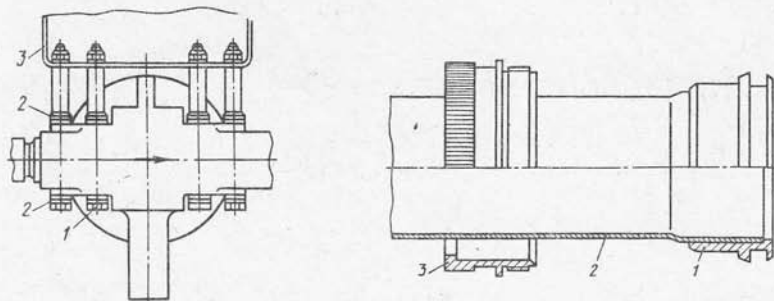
11. Установка агрегата на кронштейн с регулировочными шайбами:
